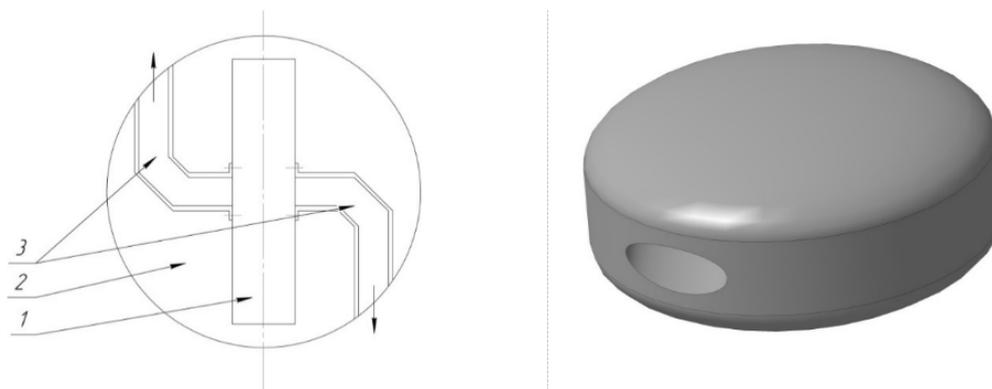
Свободнопоршневая система стабилизации тормозного устройства для спуска в атмосфере планет (вид сверху и 3d): 1 – свободнопоршневой генератор рабочего тела; 2 – защитный корпус; 3 – защитный корпус (2), выхлопные патрубки
